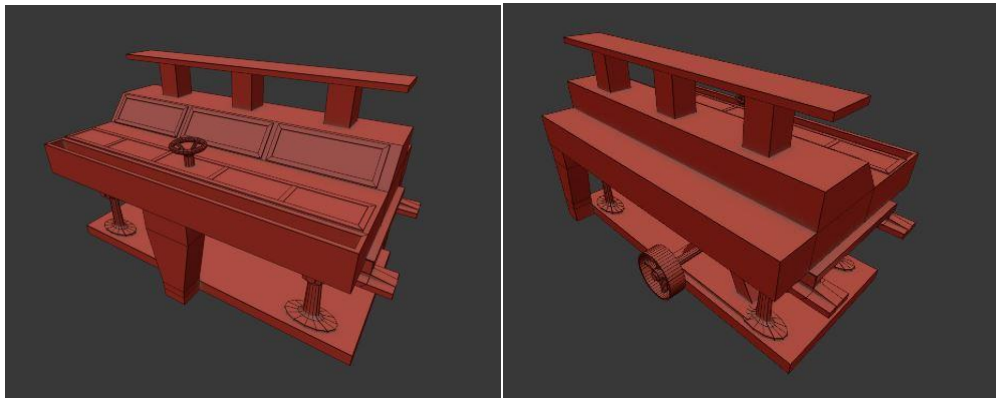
Vista frontal (izq.) y trasera (dcha.) del modelado de la deschinadora.
